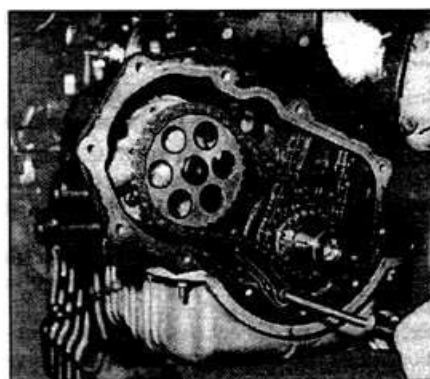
Вывертывание болта крепления натяжителя цепи привода масляного насоса
